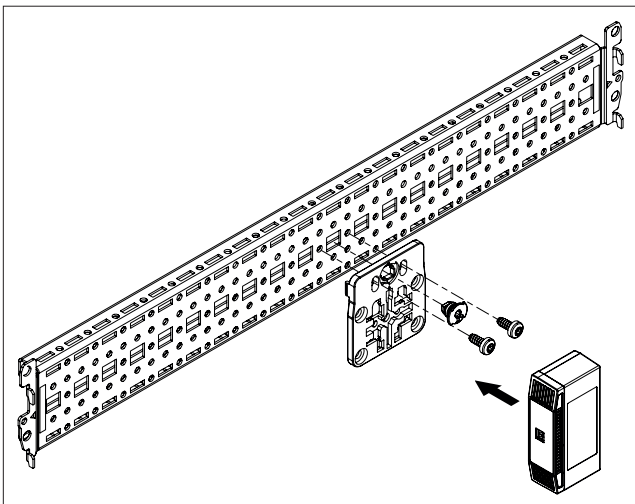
Befestigen des Sensors auf einem System-Chassis
